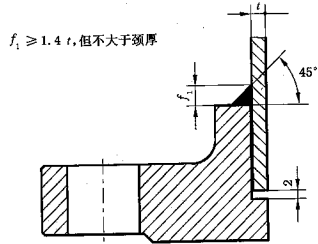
承插焊法兰与钢管的焊接连接
